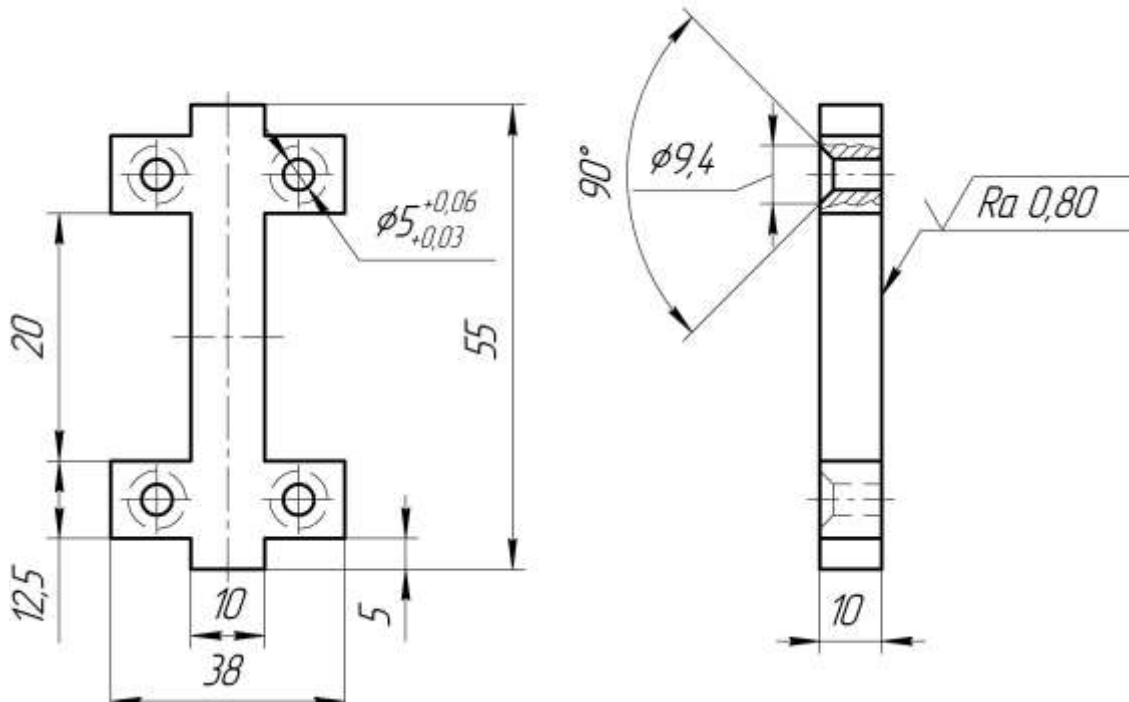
Приспособление для равномерного нагружения полимерных пленок при испытаниях на сжатие [202]
